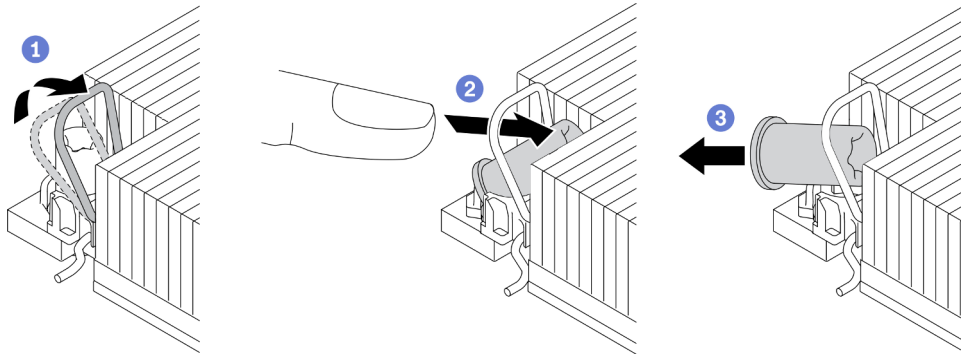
Entfernen einer T30-Torx-Mutter vom Kühlkörper
